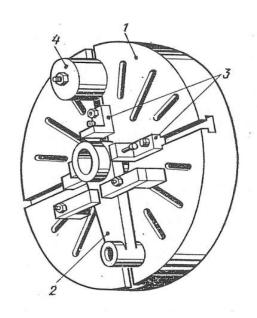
\Pi$ ланшайба: 1 -корпус; 2 -заготовка; 3 -угольники; 4 -противовес
